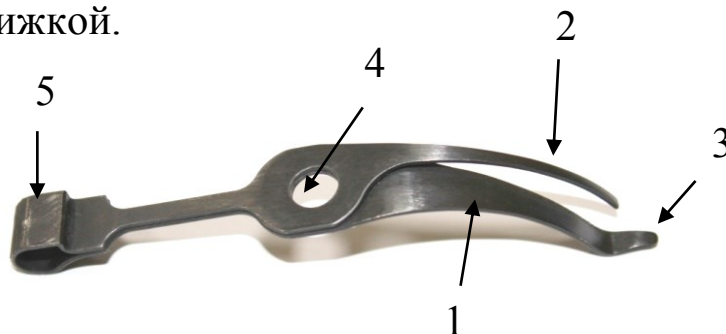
Боевая пружина: 1 – широкое перо; 2 – узкое перо; 3 – отбойный конец; 4 – отверстие; 5 – защелка
